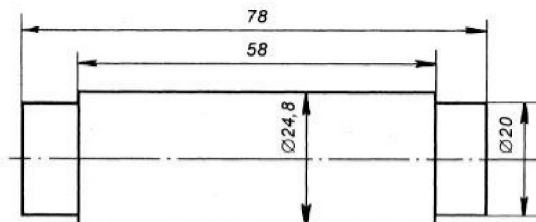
Оправка для запрессовки поршневого пальца в поршень и шатун.
